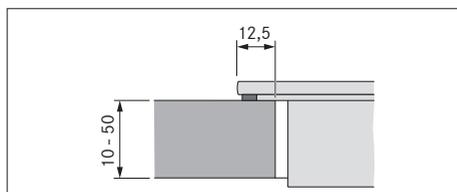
Dimension de la surface de pose pour un montage posé
